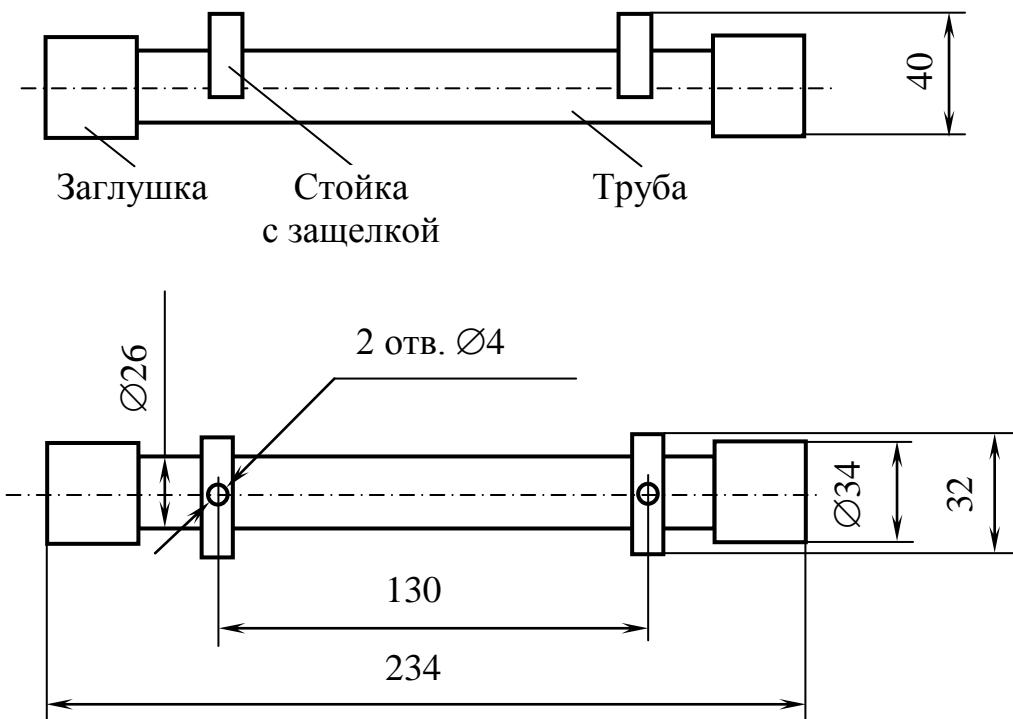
Габаритные и присоединительные размеры пенала модуля токового выхода
